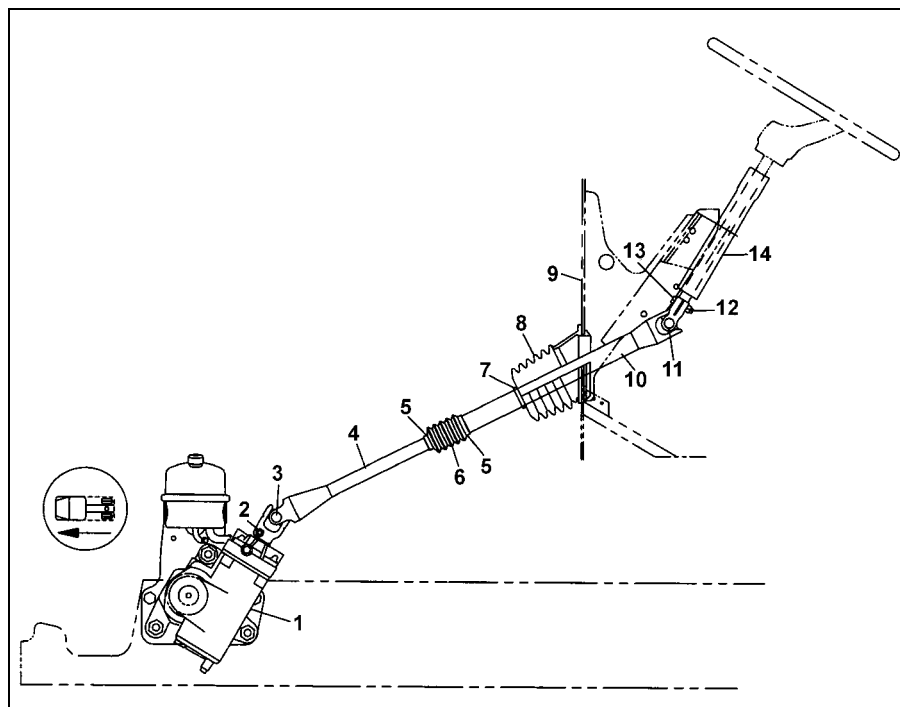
Карданная передача рулевого управления. 1 - рулевой механизм, 2 - стяжной болт, 3 - нижний карданный шарнир, 4 - внутренний вал, 5 - хомут чехла, 6 - нижний чехол карданной передачи, 7 - втулка верхнего чехла карданной передачи, 8 - верхний чехол карданной передачи, 9 - перегородка моторного отсека, 10 - внешний вал, 11 - верхний карданный шарнир, 12 - гайка стяжного болта, 13 - стяжной болт, 14 - рулевая колонка.
